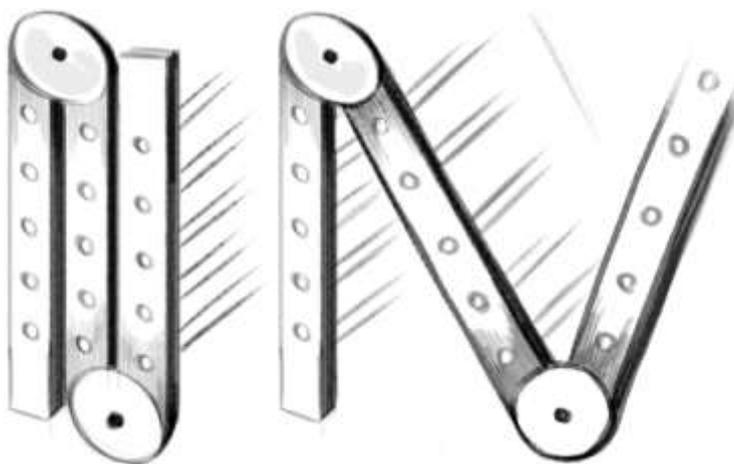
Эскиз шарнирной конструкции лестницы
